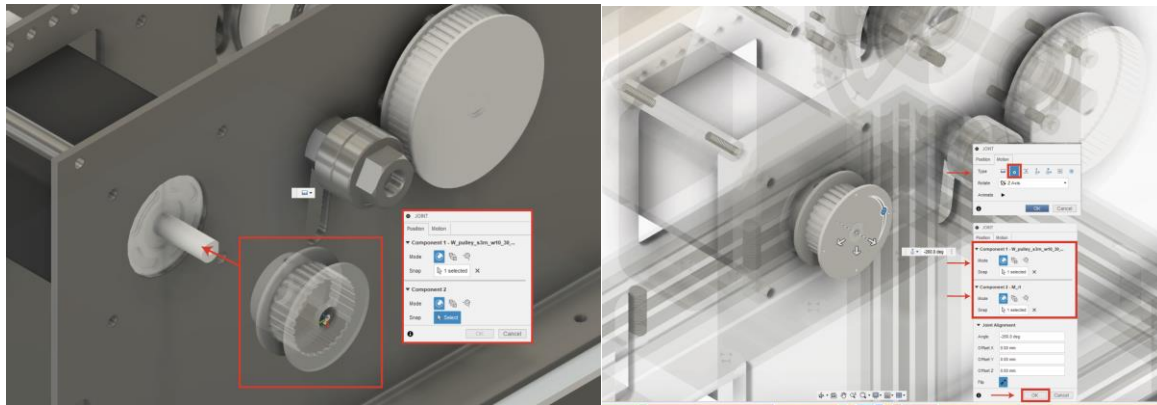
joint 예시 (pulley and shaft 간의 구속 조건 부여 – revolute)
